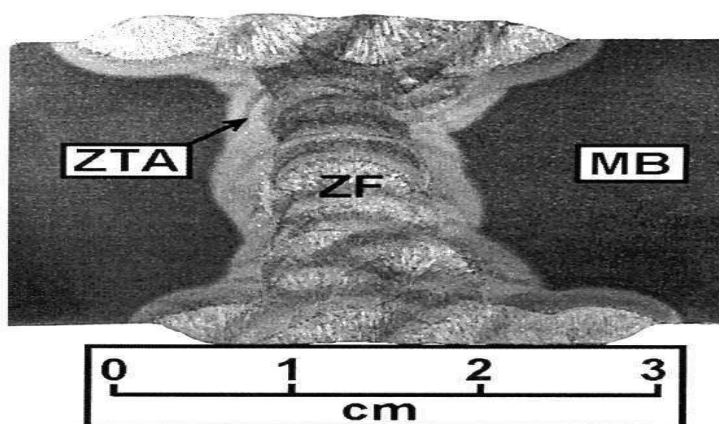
Seção transversal (macrografia) de uma solda real de vários passes⁽⁷⁾.
